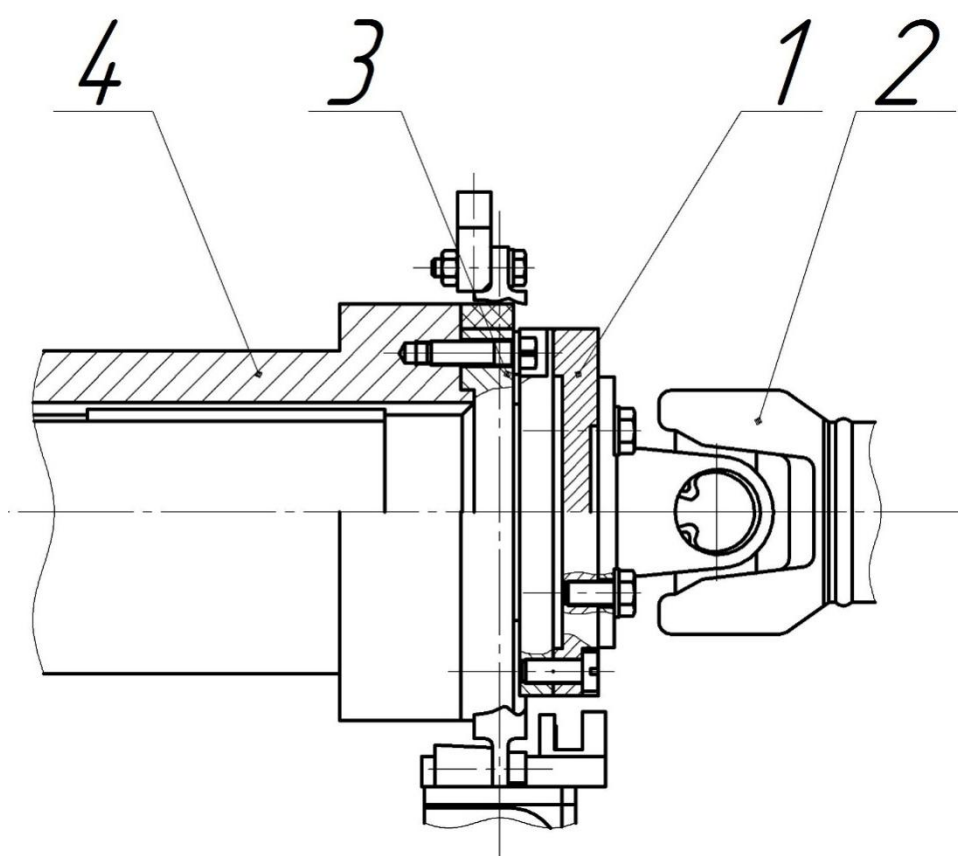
Конструкция станда для обкатки ДВС:
